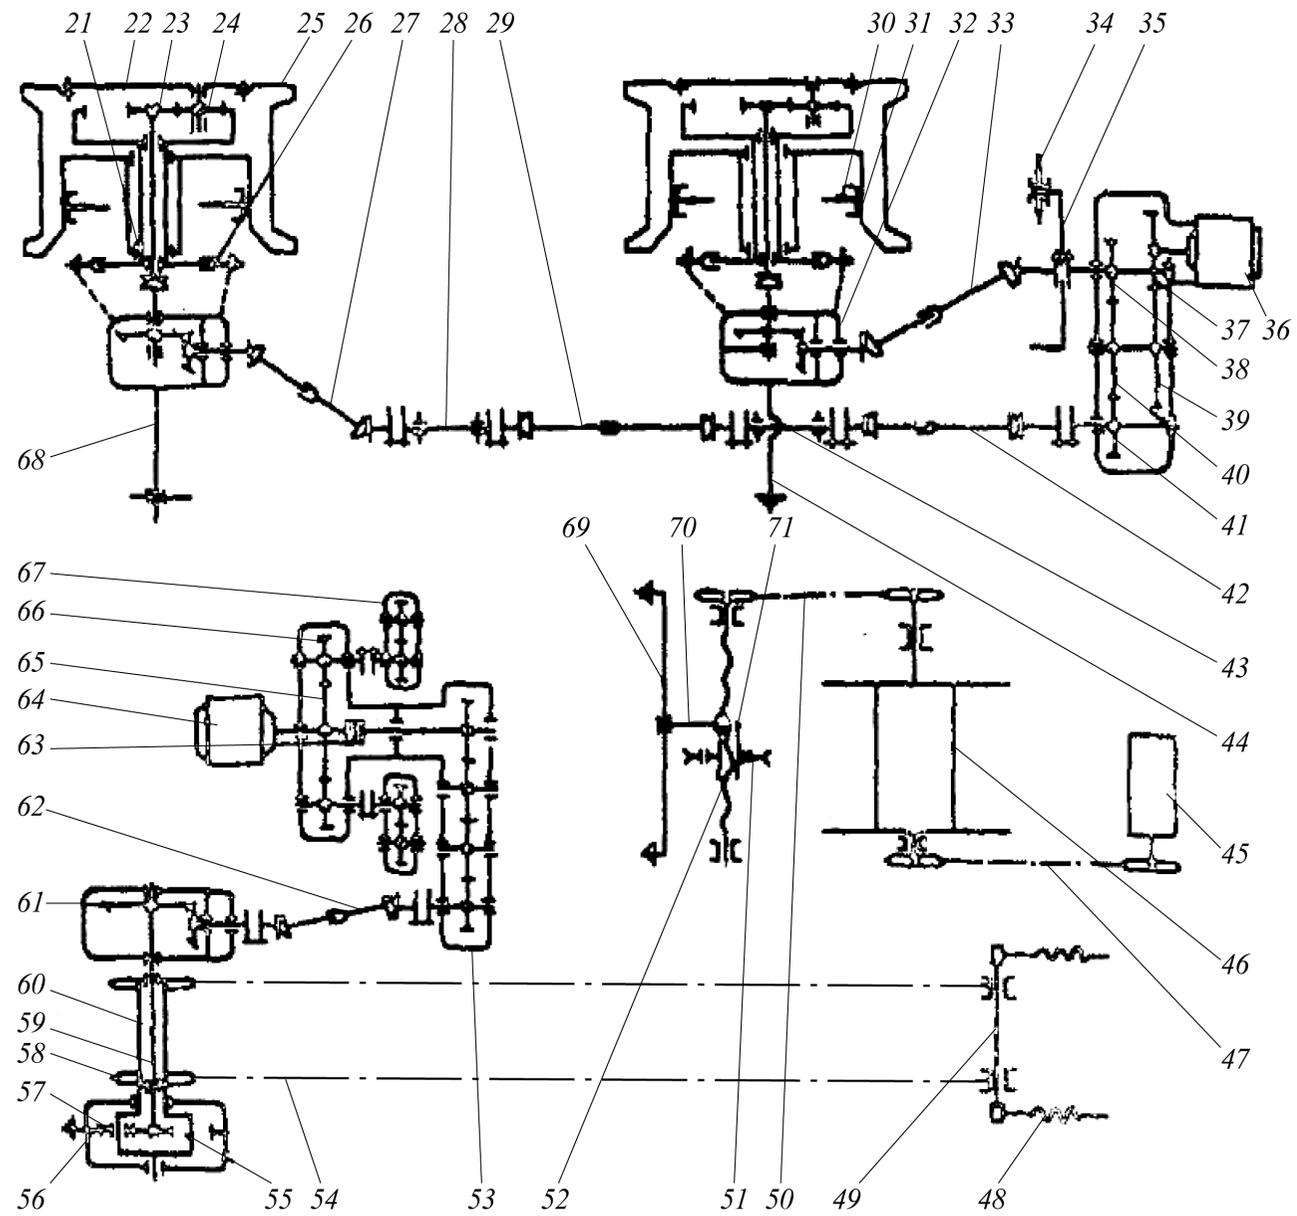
Кинематическая схема шахтного самоходного вагона 5BC-15M (расшифровка обозначений приведена в тексте)
